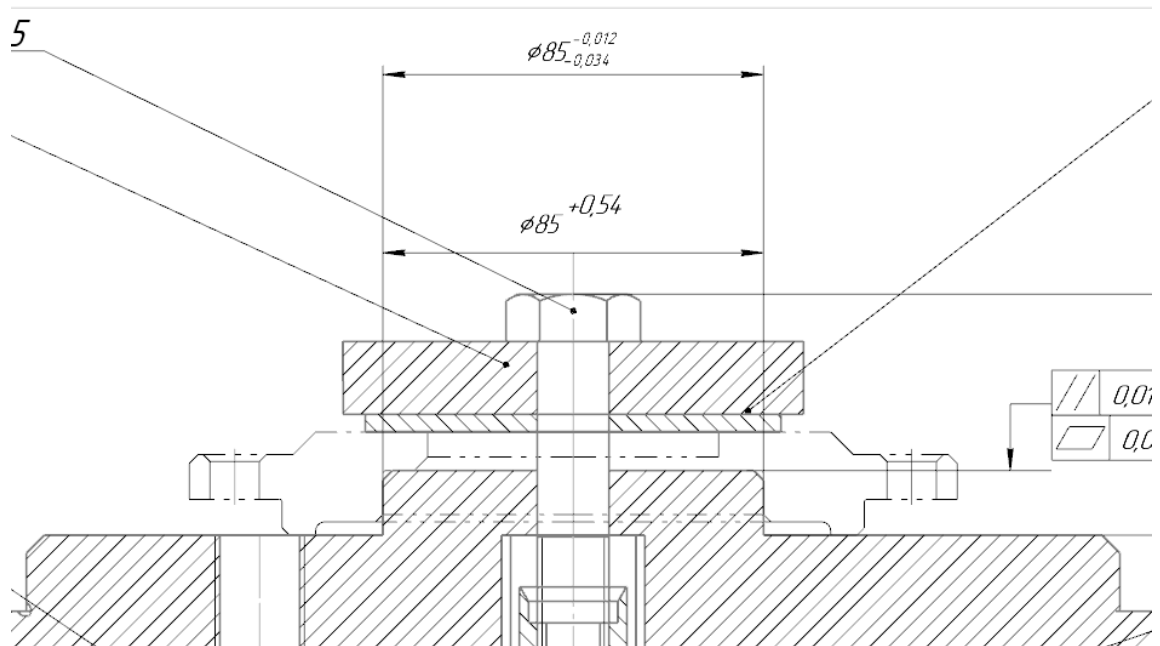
Ескіз для визначення зазору між внутрішньою поверхнею деталі та установчим стаканом
